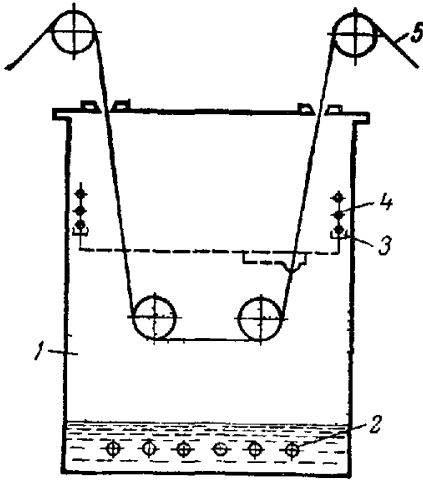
Схема установки непрерывного обезжиривания металлической ленты, фольги, ткани и т. д.:
